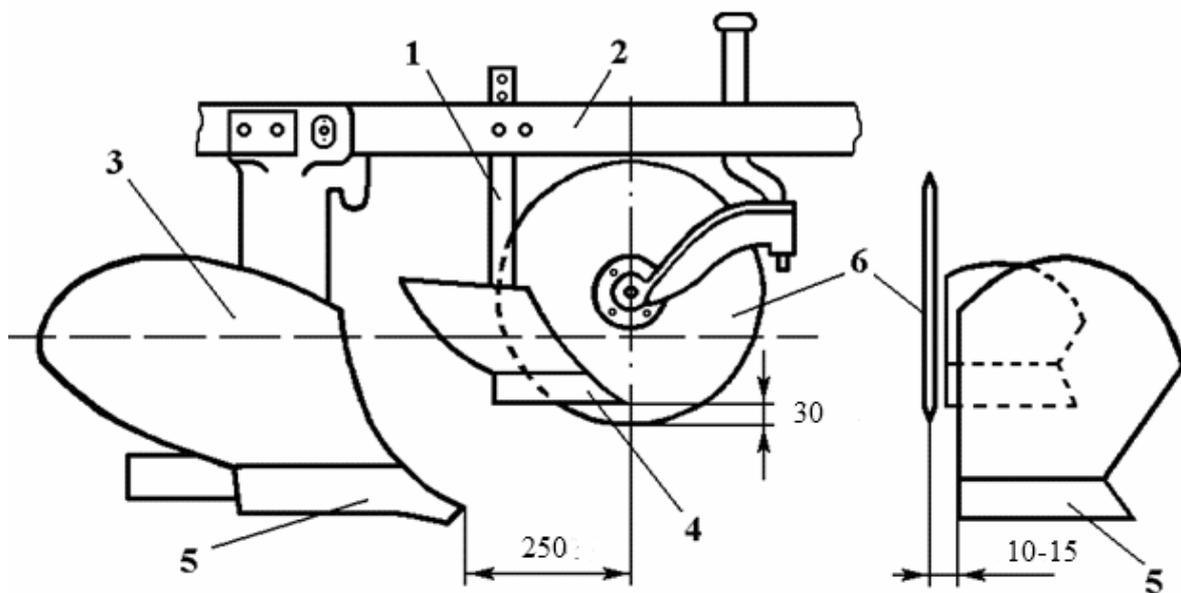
Схема установки дискового ножа и предплужника на раме плуга
